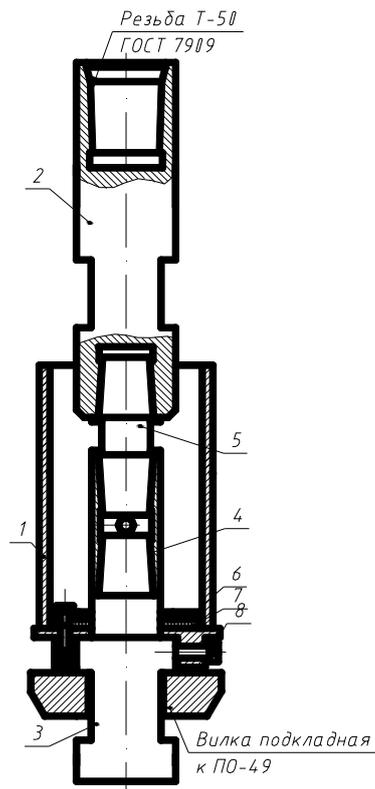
Приставка к стенду для определения средней наработки замковой резьбы на отказ
